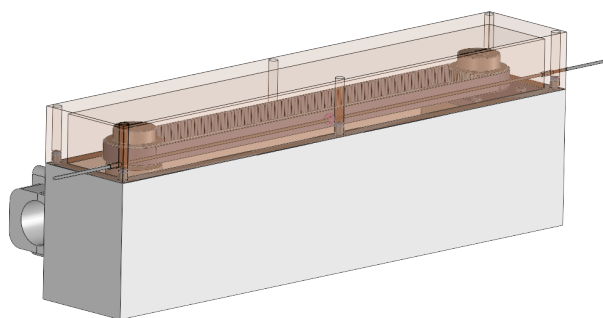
Vista general del diseño de carcasa ensamblada.
